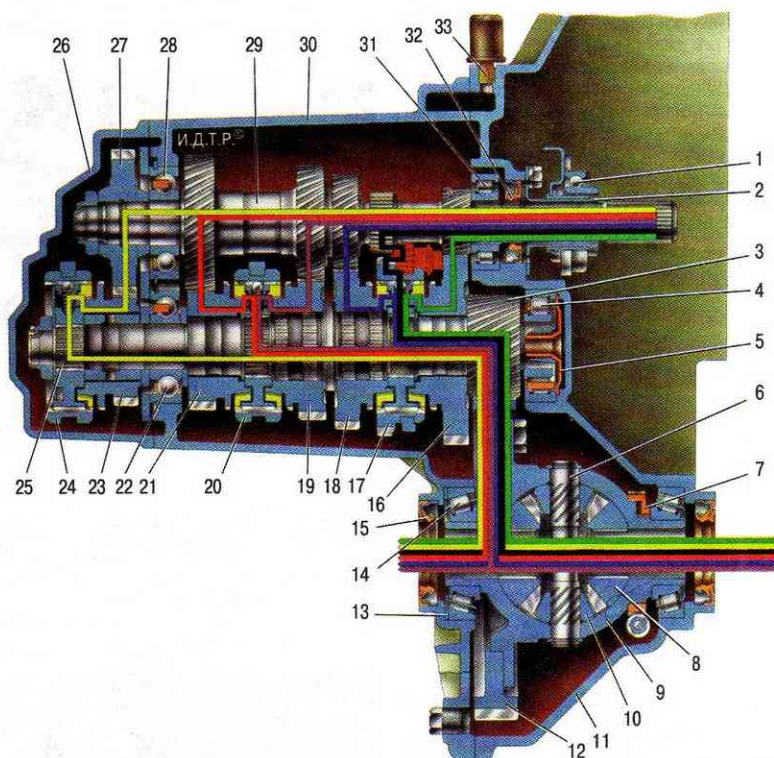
Коробка передач: 1 — подшипник выключения сцепления; 2 — направляющая втулка муфты подшипника выключения сцепления; 3 — шестерня ведущая главной передачи; 4 — роликовый подшипник вторичного вала; 5 — маслобросник; 6 — ось сателлитов; 7 — ведущая шестерня привода спидометра; 8 — шестерня полуоси; 9 — коробка дифференциала; 10 — сателлит; 11 — картер сцепления; 12 — ведомая шестерня главной передачи; 13 — регулировочное кольцо; 14 — роликовый конический подшипник дифференциала; 15 — сальник полуоси; 16 — ведомая шестерня I передачи вторичного вала; 17 — синхронизатор I и II передач; 18 — ведомая шестерня II передачи вторичного вала; 19 — ведомая шестерня III передачи вторичного вала; 20 — синхронизатор III и IV передач; 21 — ведомая шестерня IV передачи вторичного вала; 22 — шариковый подшипник вторичного вала; 23 — ведомая шестерня V передачи вторичного вала; 24 — синхронизатор V передачи; 25 — вторичный вал; 26 — задняя крышка картера коробки передач; 27 — ведущая шестерня V передачи; 28 — шариковый подшипник первичного вала; 29 — первичный вал; 30 — картер коробки передач; 31 — роликовый подшипник первичного вала; 32 — сальник первичного вала; 33 — сапун
